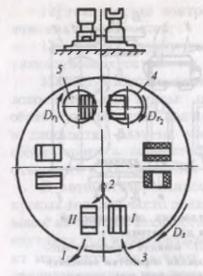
Схема обработки плоскостей на карусельнофрезерном станке с перекладыванием заготовок
